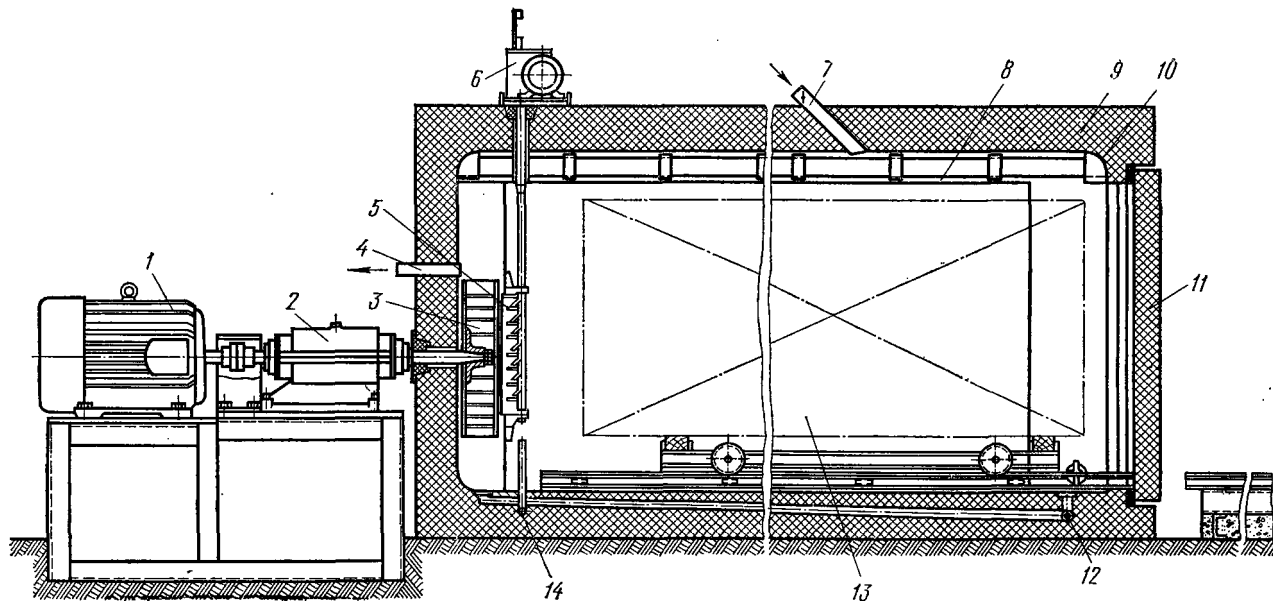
Нагревательная установка типа ПАП для сушки пиломатериалов:
